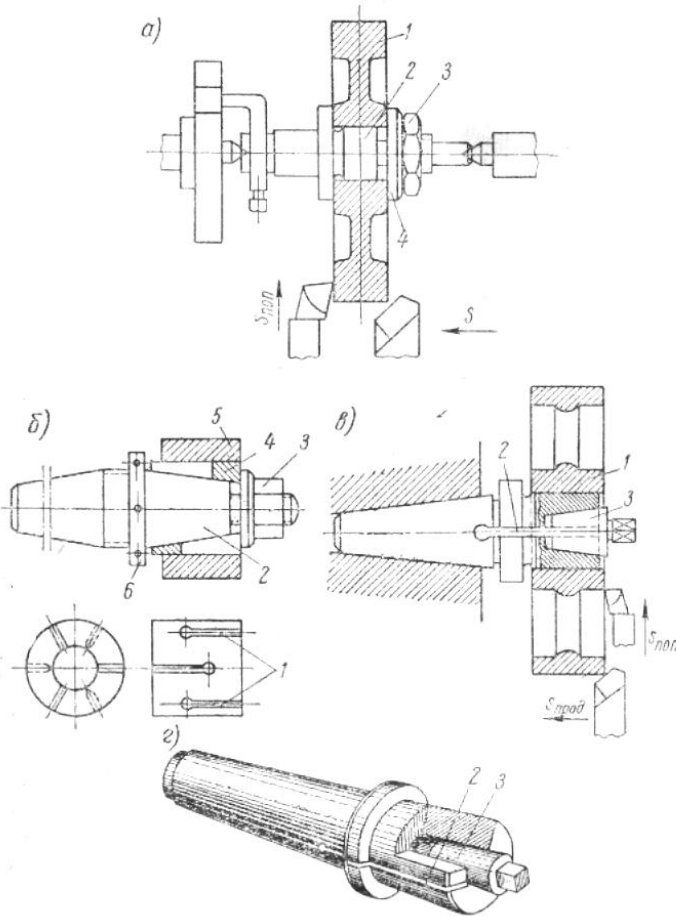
Оправки для закрепления деталей: а) – цельная цилиндрическая; б)-разжимная с разрезанной упругой гильзой; в,г.) –консольная разжимная
